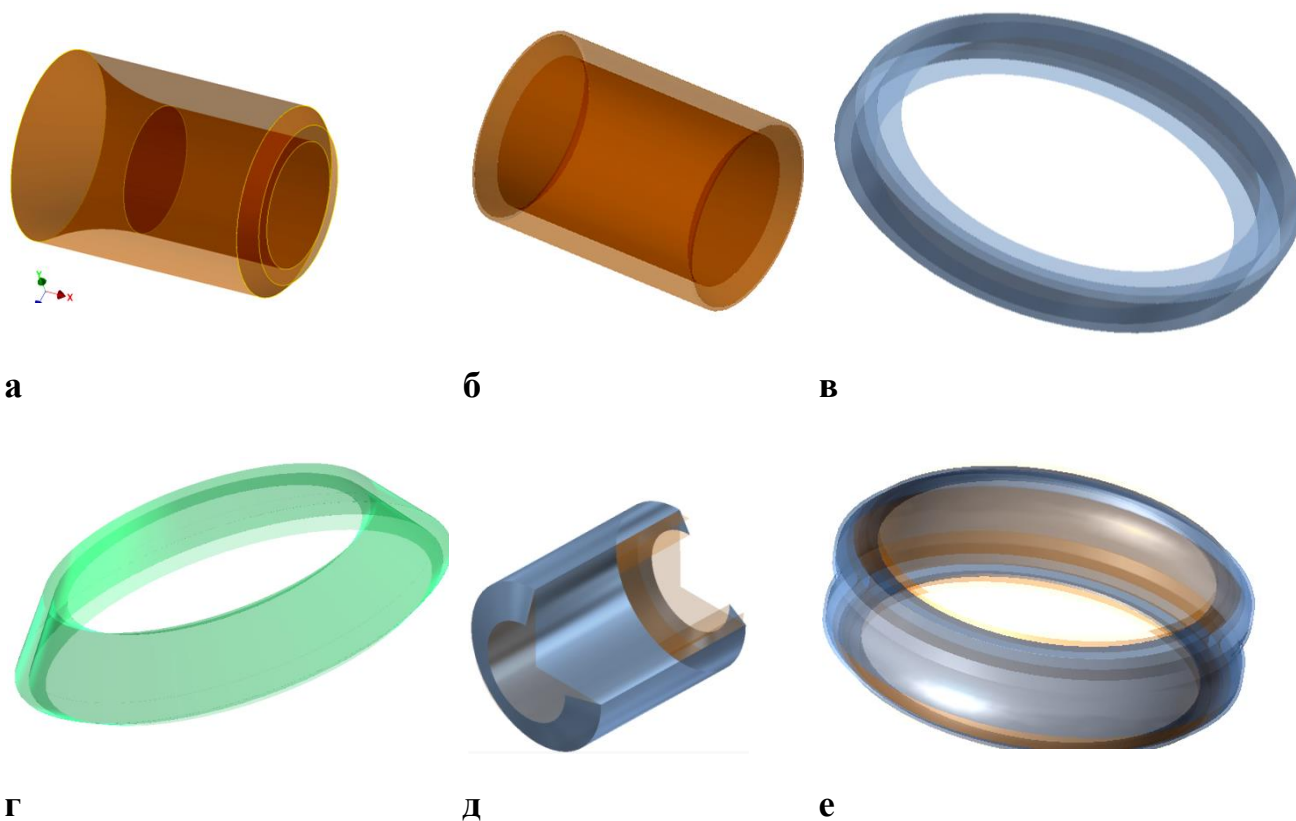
Трехмерные модели параметрических оболочек зубчатых венцов: а – зубья (шлицы) вала; б - зубья (шлицы) ступицы; в - цилиндрическая; г – коническая; д – червяка; е – червячного колеса
